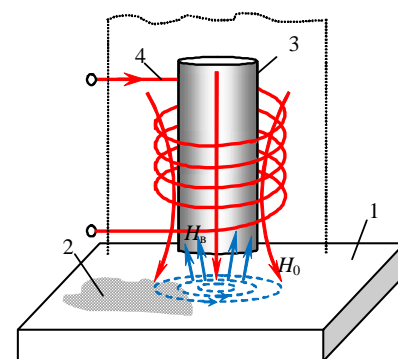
Схема ВС методу вимірювання об'єму П на поверхні виливка: 1 – виливок, 2 – механічний П; 3 – сердечник; 4 – котушка індуктивності
